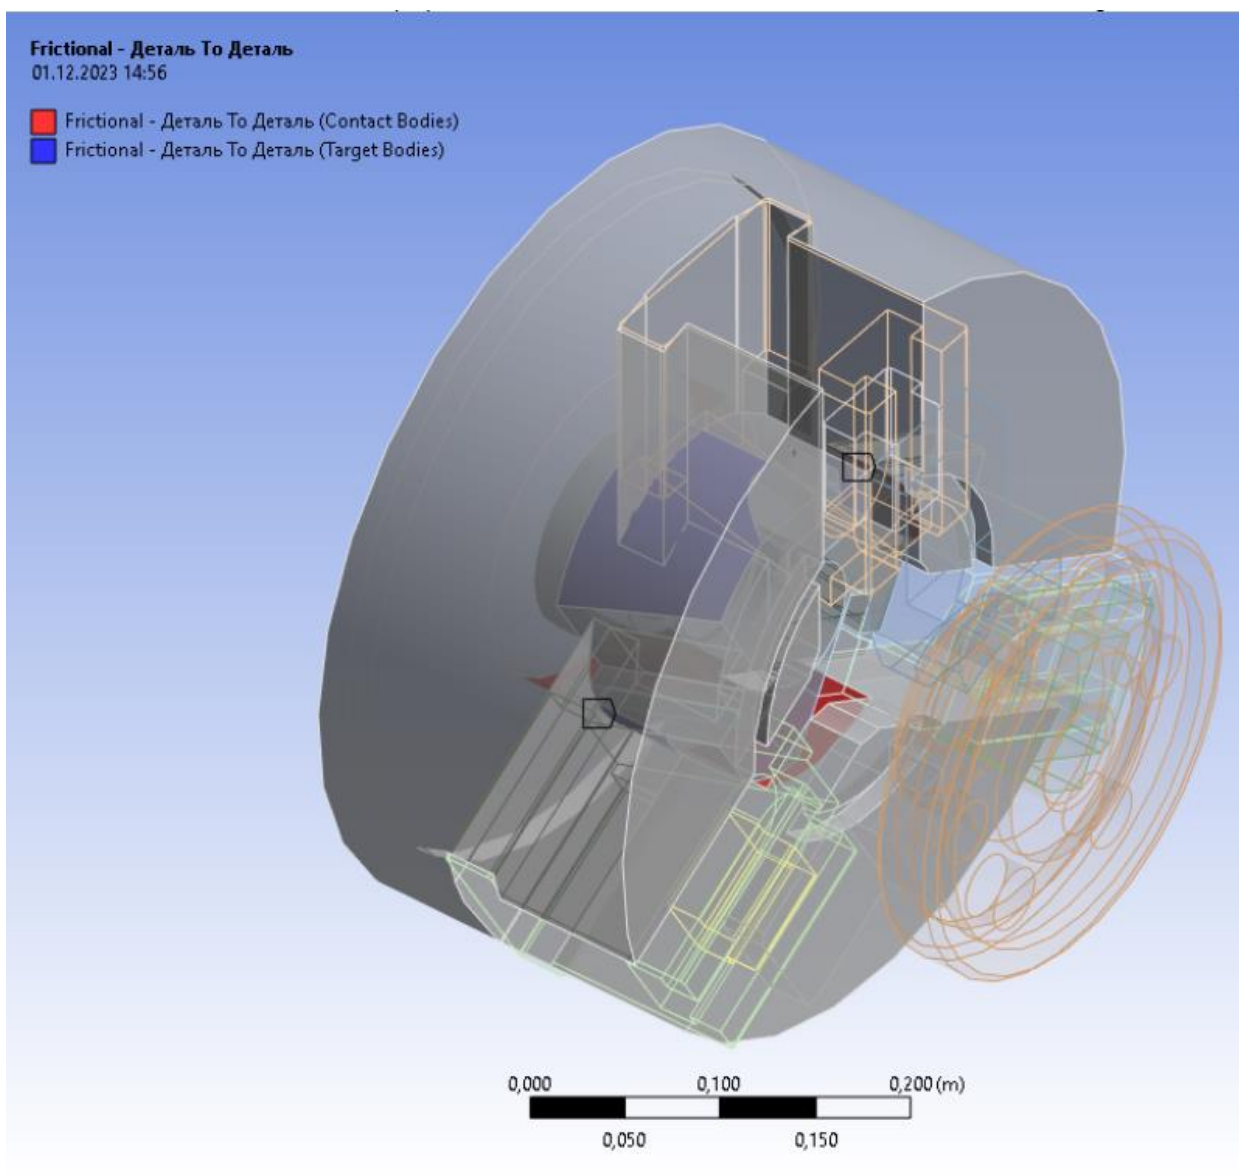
Сполучення поверхні стакану з поверхнею корпусу пристрою
